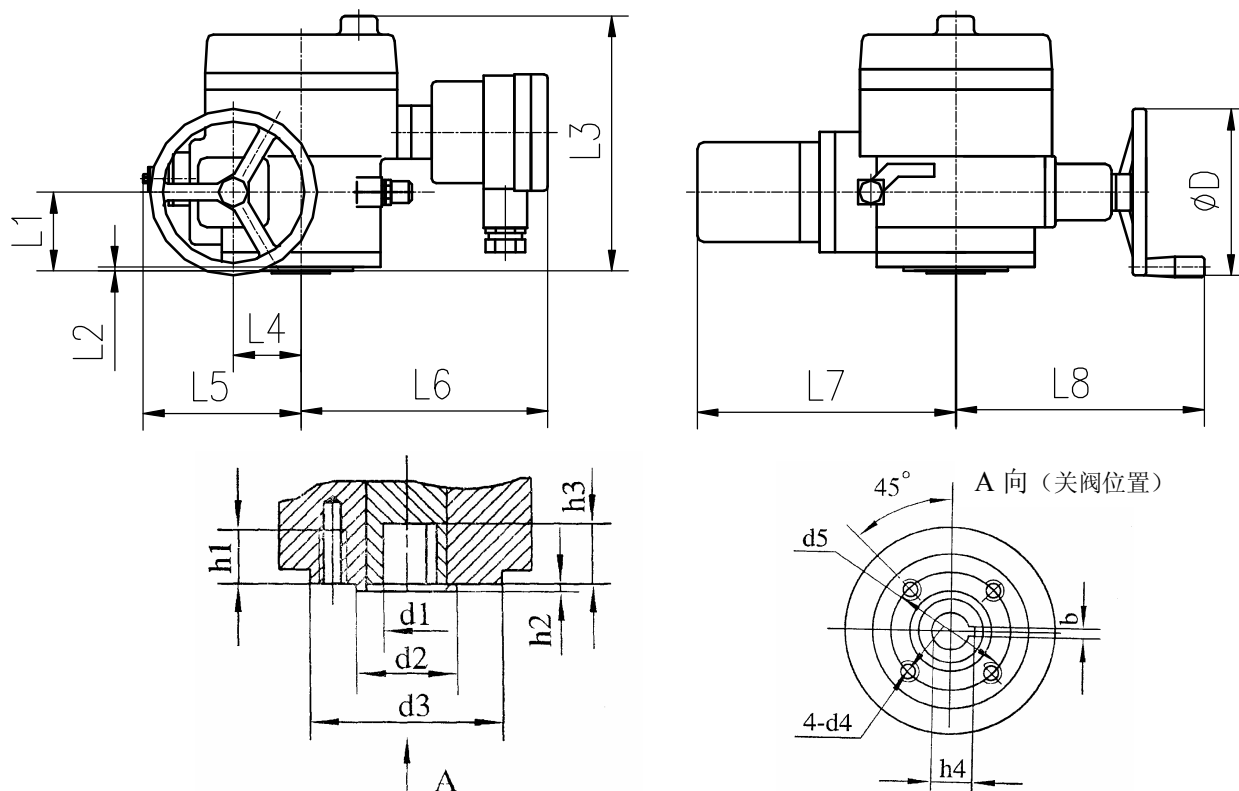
外形及连接尺寸图 Fig.2 overall size and connection dimensions
